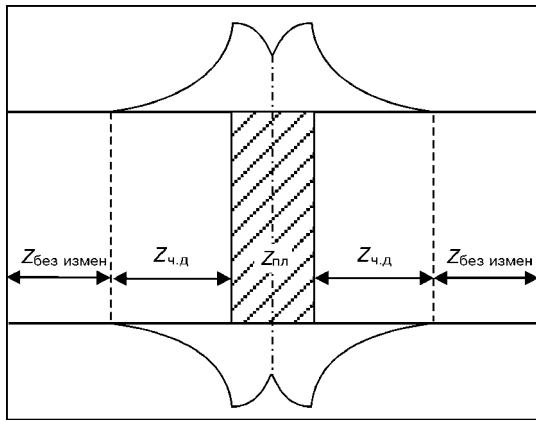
Зоны сварного соединения, выполненного сваркой трением
